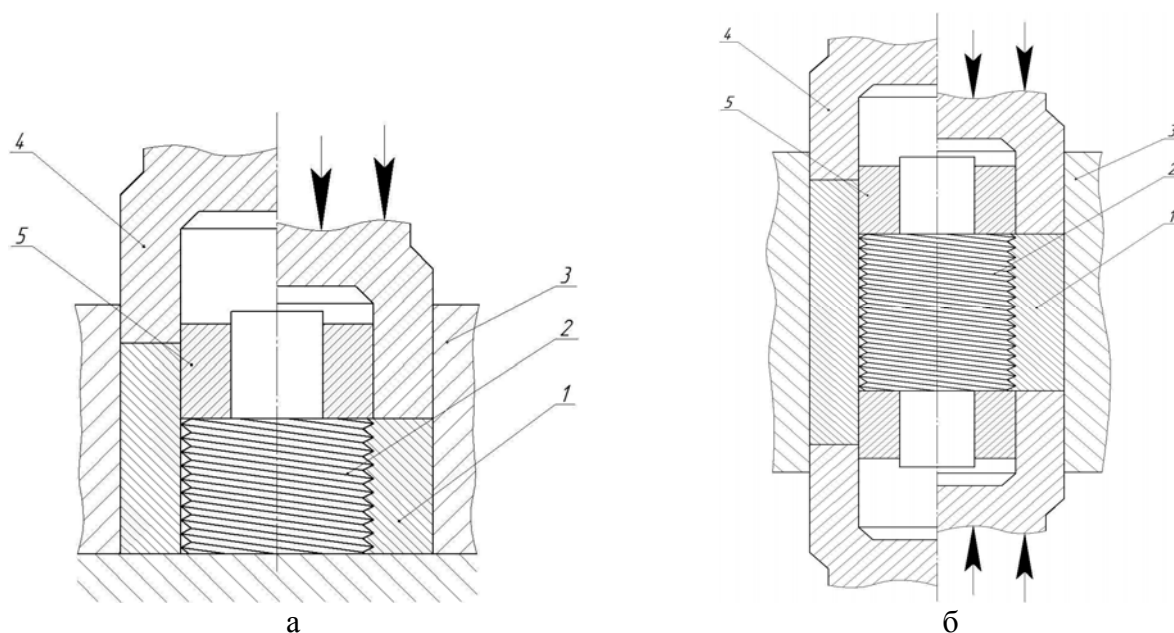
Способ бокового выдавливания резьбы (1 – заготовка; 2 – резьбовая оправка; 3 – матрица; 4 – пуансон; 5 – направляющая втулка):
